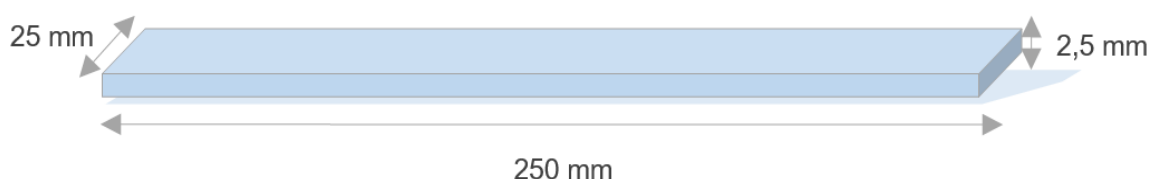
Dimensões dos corpos de prova ASTM D3039 – 17.
